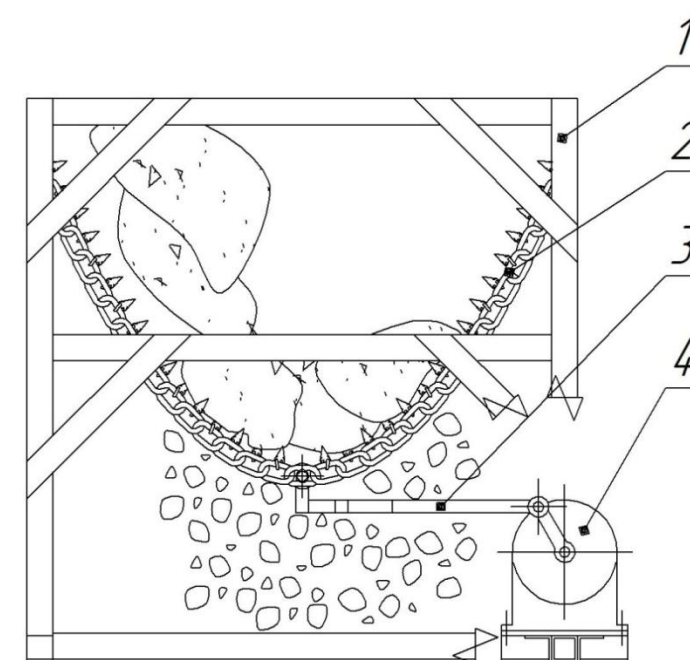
Рабочий привод цепного измельчителя: 1 – рама; 2 – рабочий орган; 3 – привод; 4 – кривошипно-шатунный механизм
